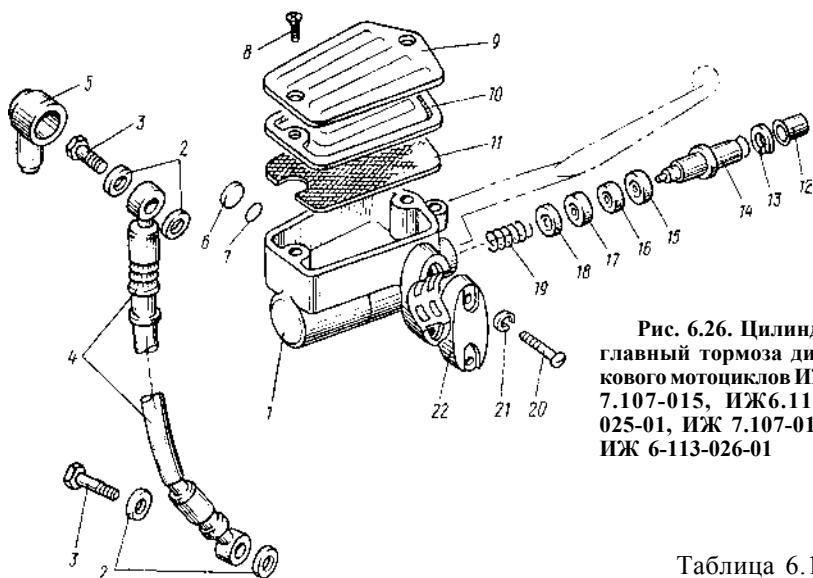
Цилиндр главный тормоза дискового мотоциклов ИЖ 7.107-015, ИЖ 6.113-025-01, ИЖ 7.107-016, ИЖ 6-113-026-01
